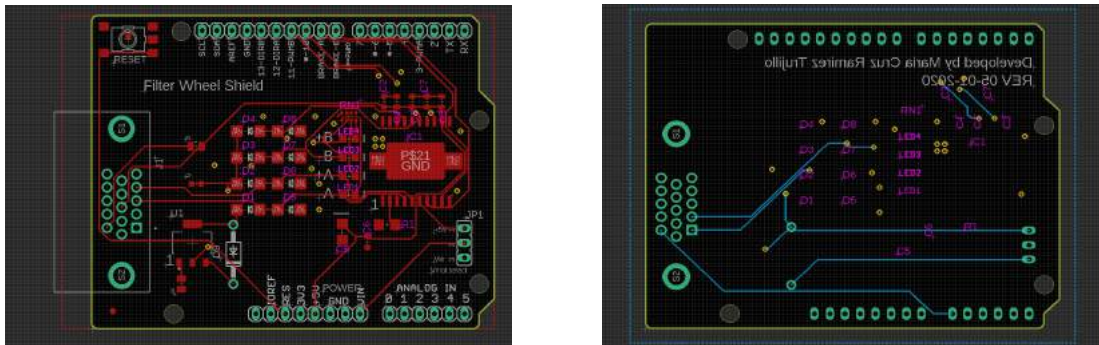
Top (izquierda) y Bottom (derecha) de la PCB diseñada
